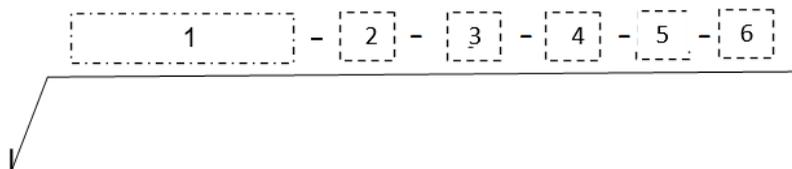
Структура условного обозначения шва сварного соединения на чертежах
